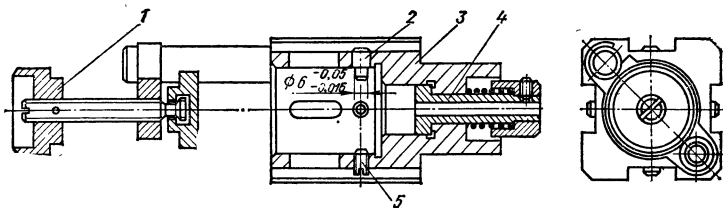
Кантующийся кондуктор для сверления отверстий, расположенных под углом  $90^\circ$
